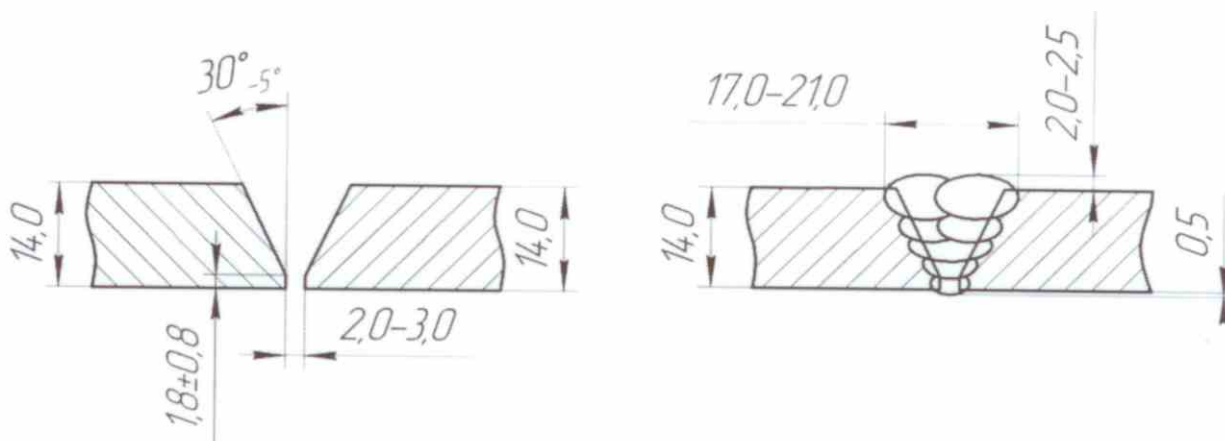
Геометрические параметры сборки и сварного шва
